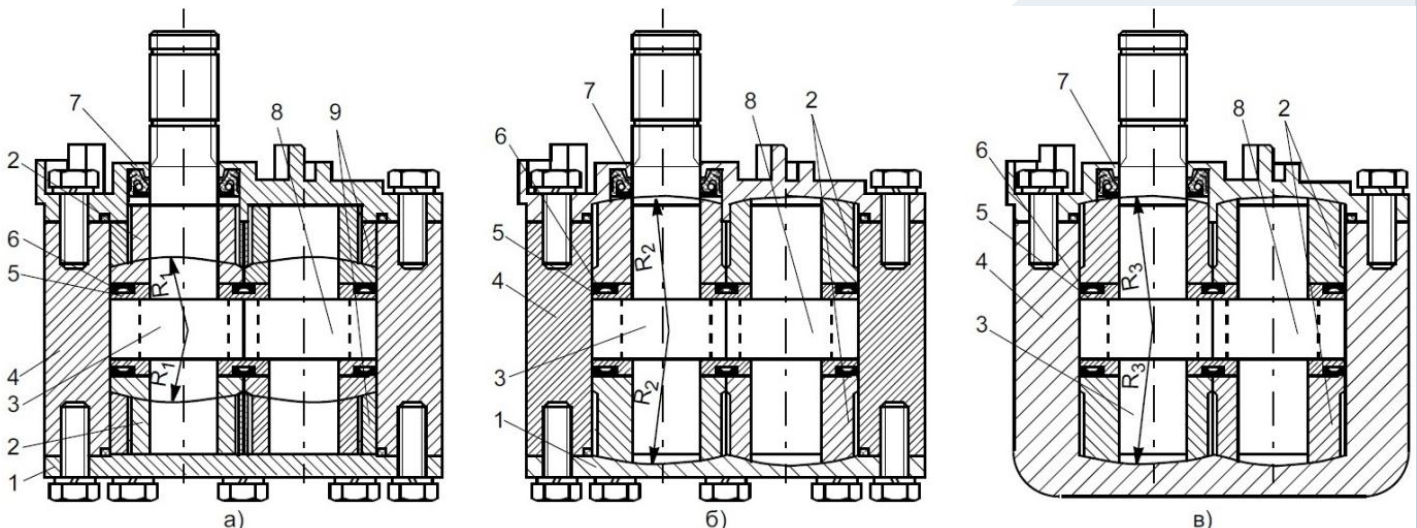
Шестеренные насосы различной компоновки с самоустанавливающимися подшипниками
